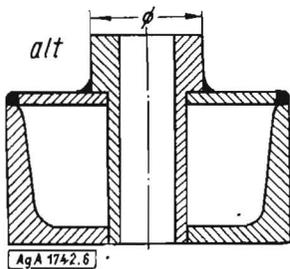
Kastenträgerkonstruktion, alte Ausführung
